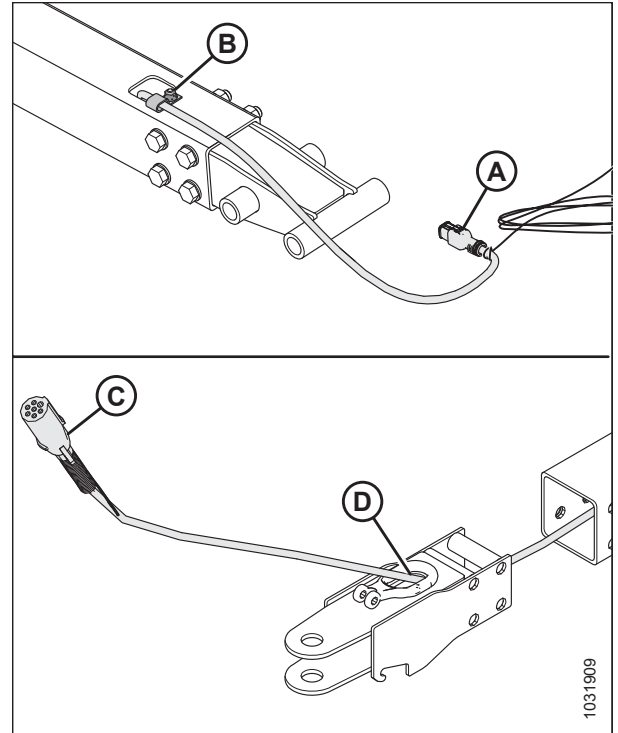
Extracción del adaptador de remolque de la horquilla
